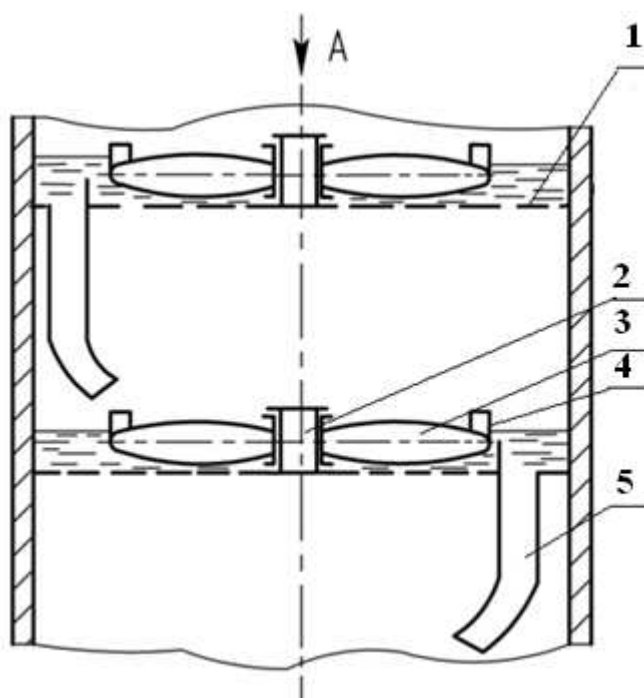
Общий вид в разрезе предлагаемой конструкции теплообменной тарелки с барботажным контактным устройством представляющей собой лопатки
